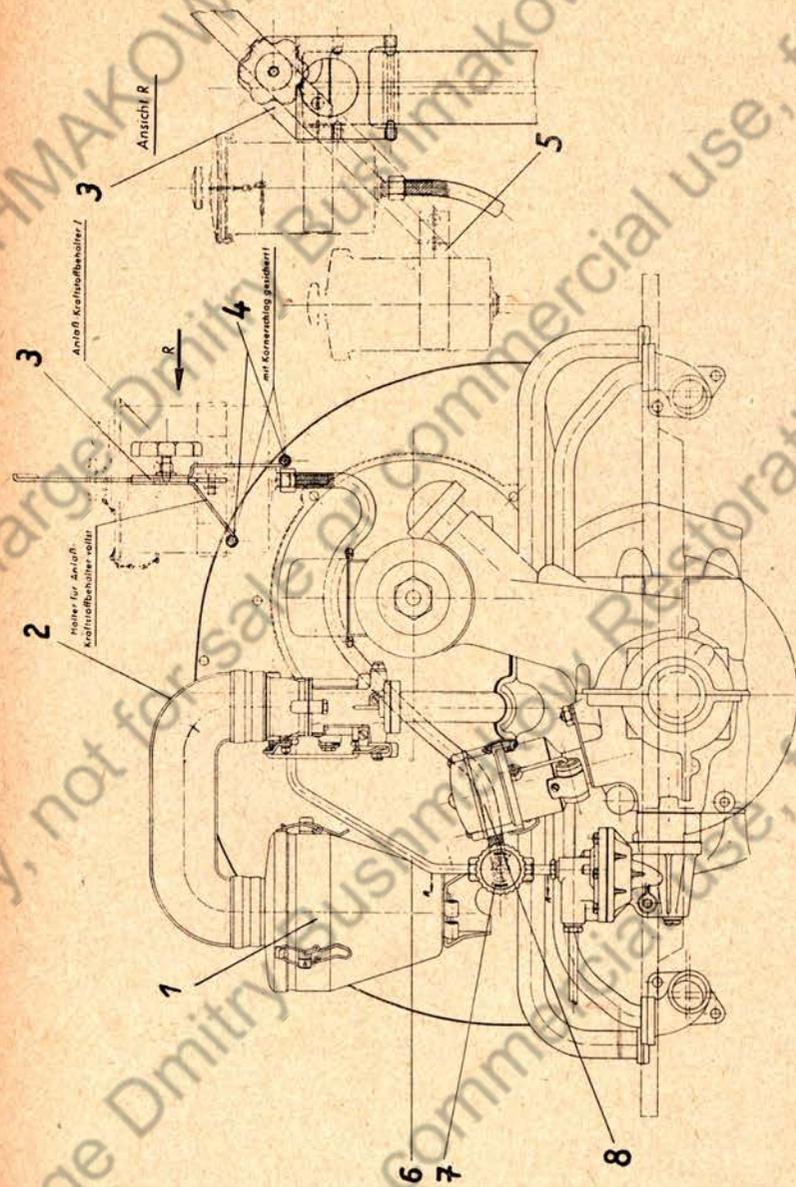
Einbau der Sonderausrüstung für Winterbetrieb, Schema
